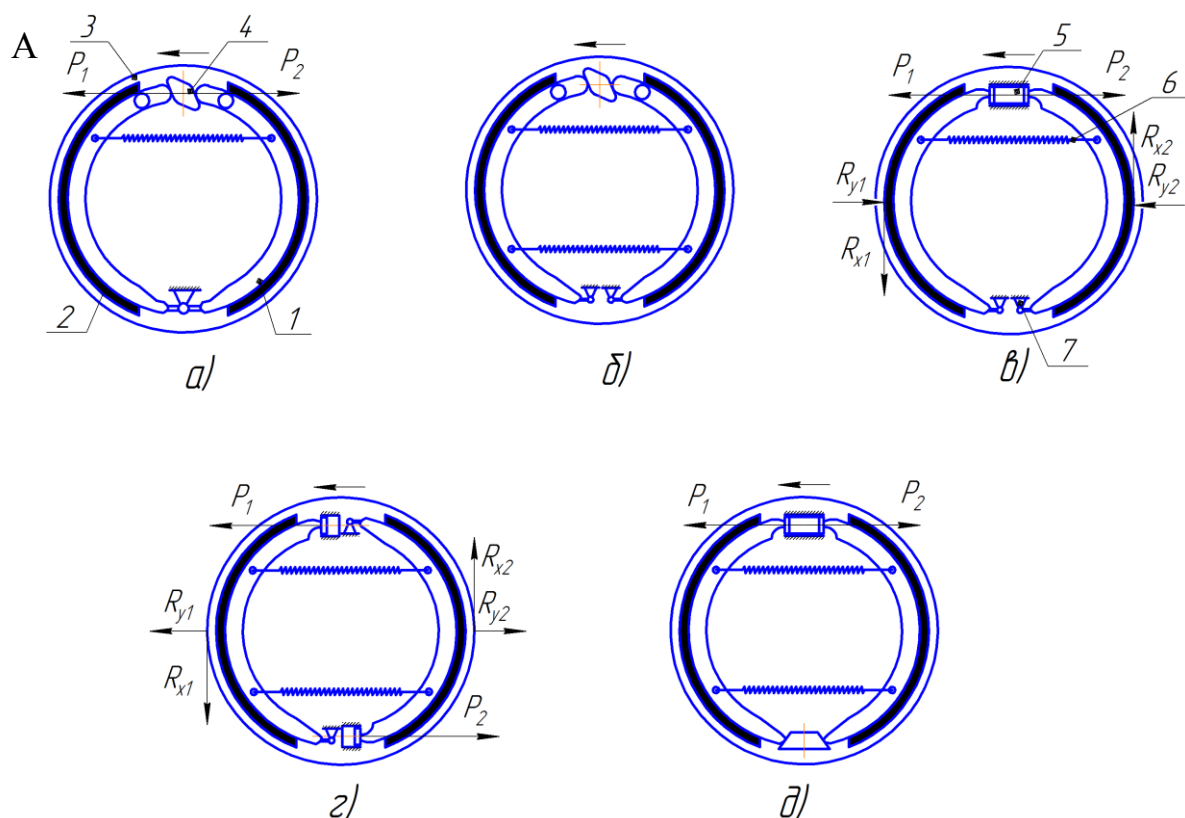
Схема крепления колодок барабанного тормозного механизма
